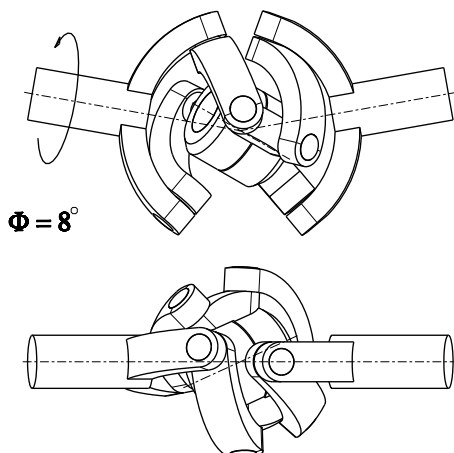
CAD model kĺbu v štartovacej polohe – pohľad spredu a pohľad zhora
